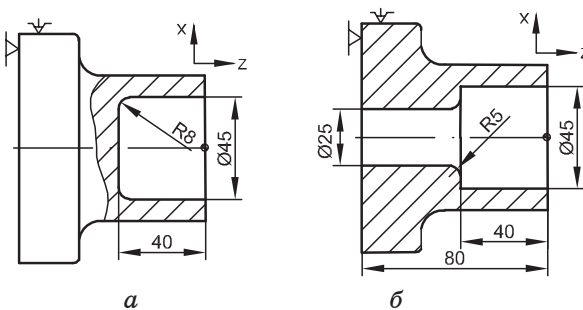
Обробка на внутрішній поверхні деталі: а — галтели; б — заокруглення
